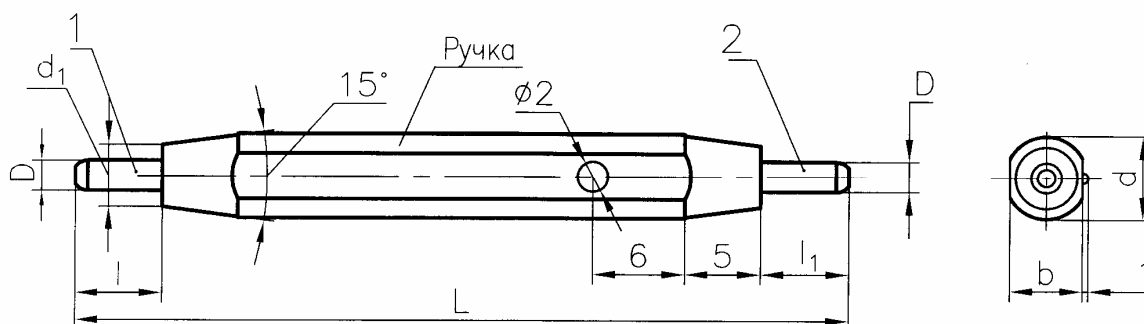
Калибр-пробка гладкий двусторонний:
